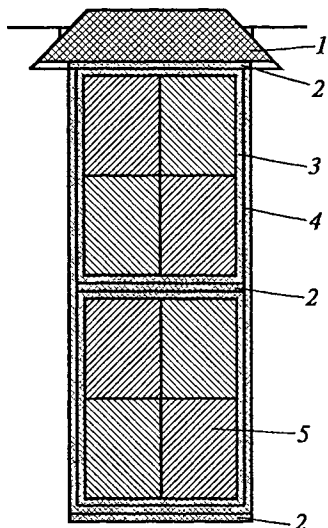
Разрез паза ДТК-800КЭ:
